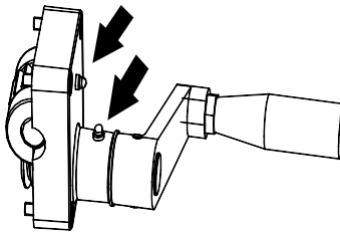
Schmierbuchsen, Schneckengetriebegehäuse
